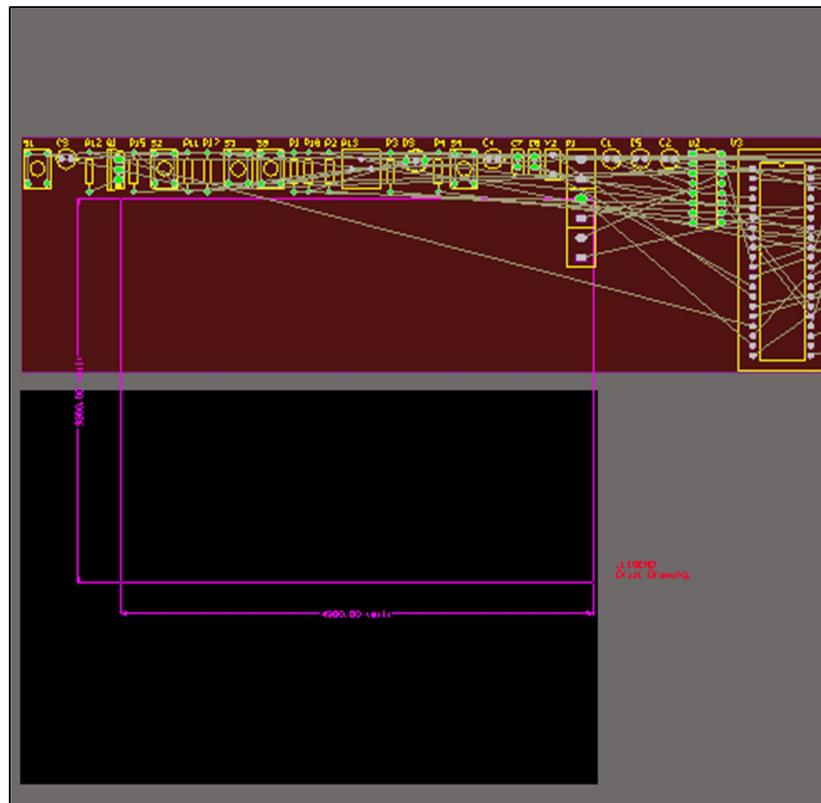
Placa PCB con los componentes antes de posicionarlos.
